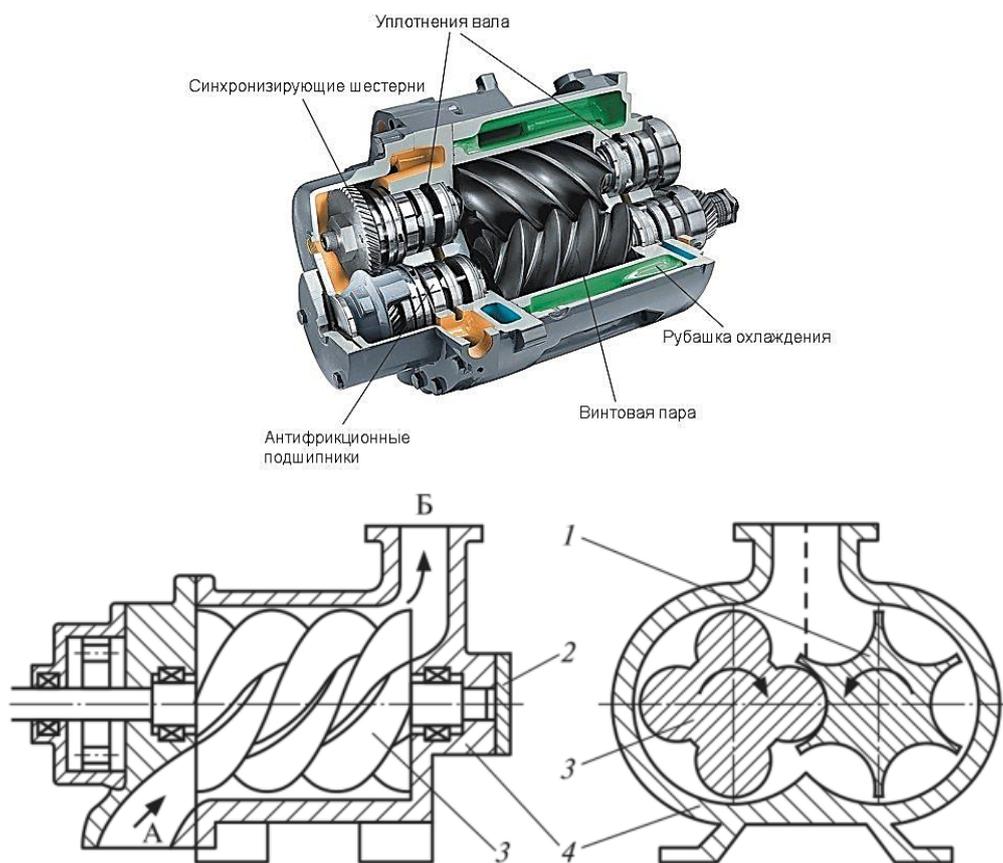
Схематическое изображение винтового блока воздушного компрессора
